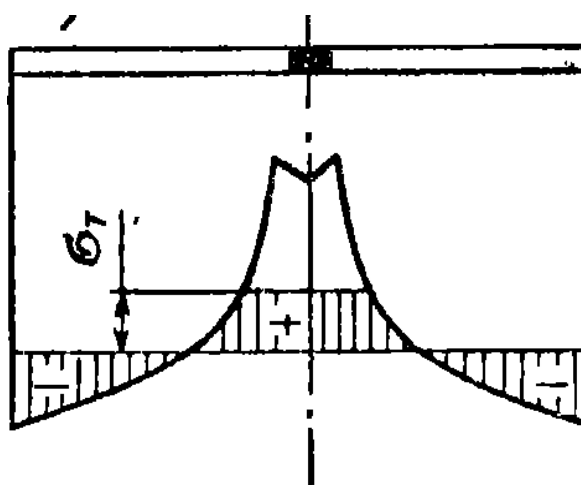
Сварка встык двух полос равной ширины
